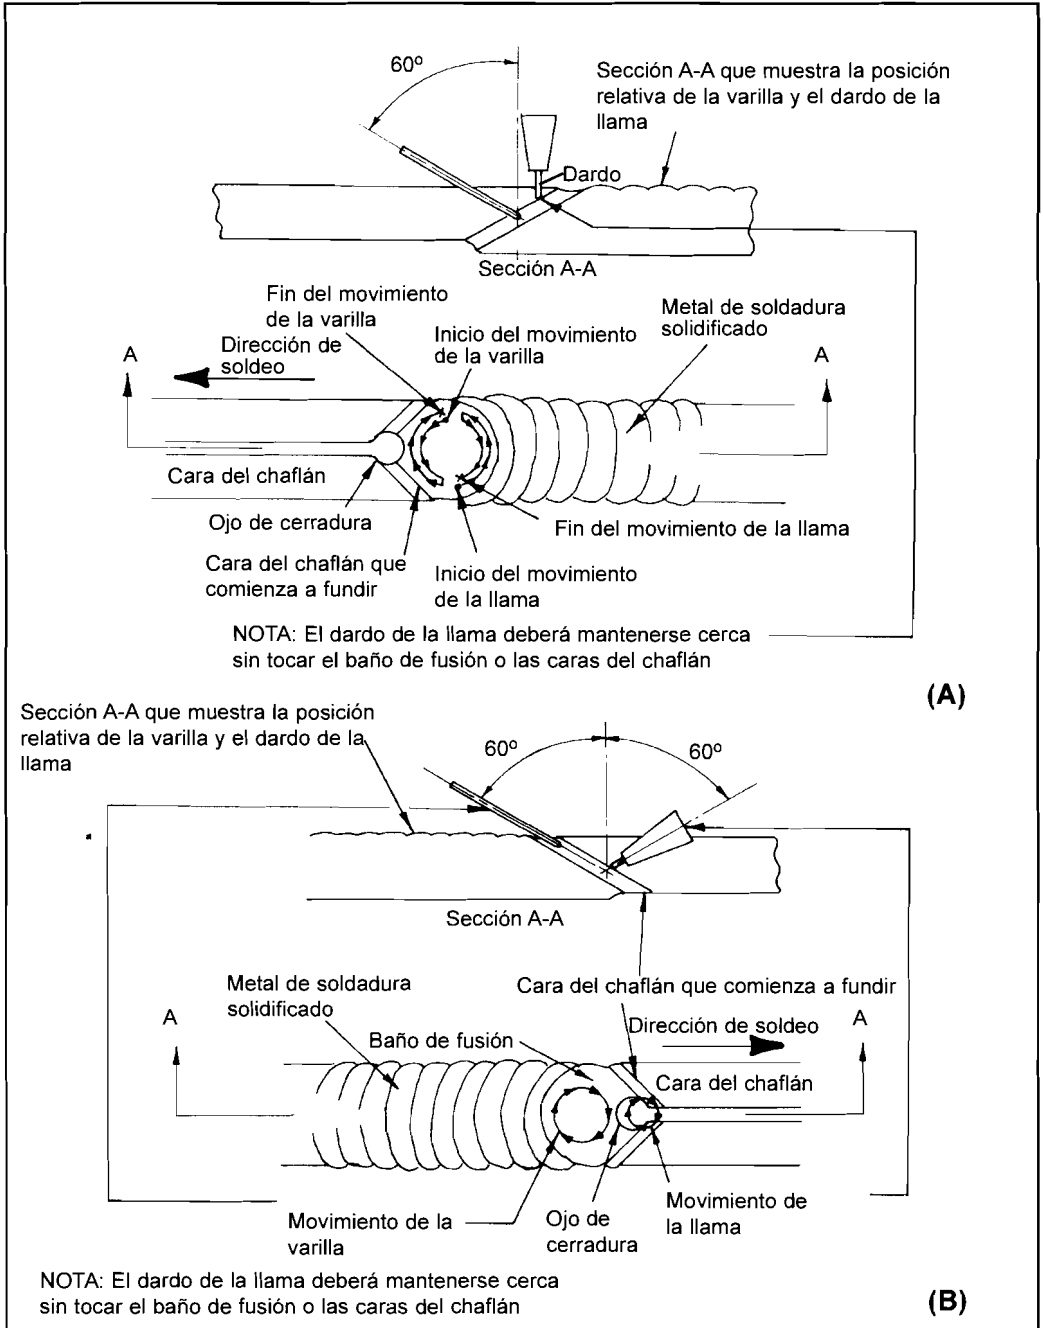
(A) TÉCNICA DE SOLDEO HACIA ADELANTE O A IZQUIERDAS.
